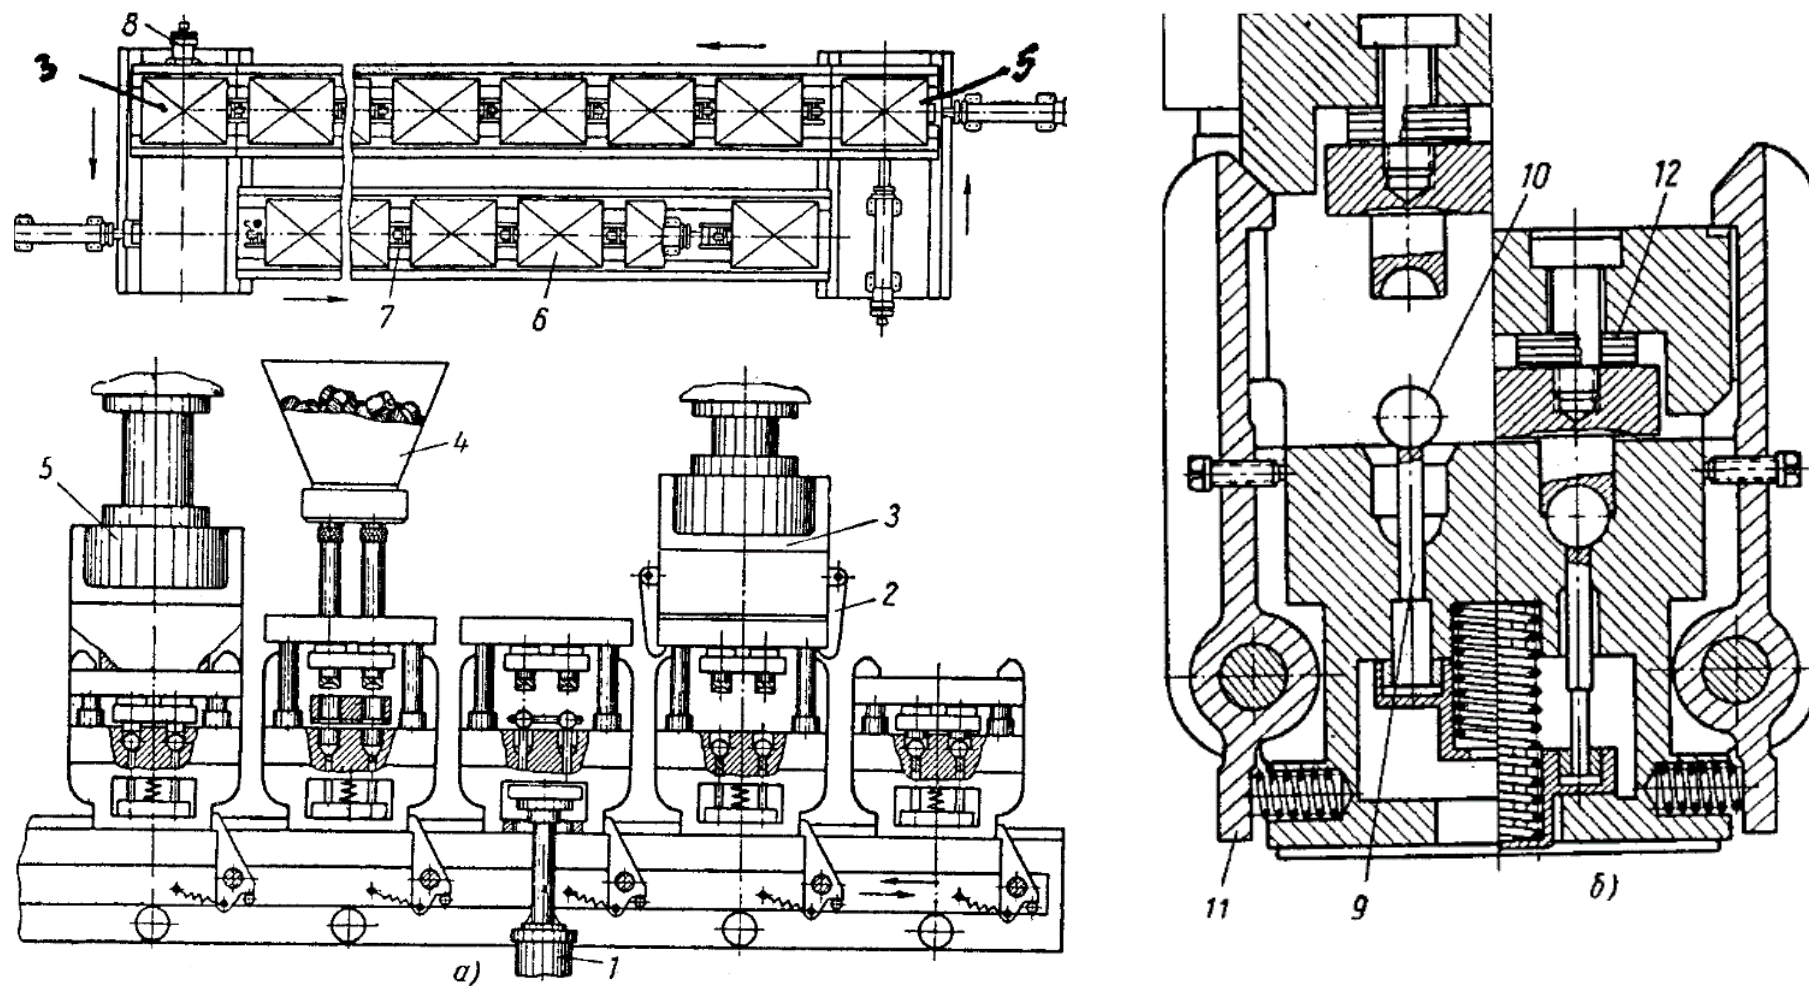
Автоматическая прессовая линия с выносными пресс-формами: *а* – общий вид; *б* – пресс-форма; 1 – гидроцилиндр выталкивания готовых изделий; 2 – захваты-держатели пуансона; 3 – пресс раскрытия пресс-формы; 4 – питатель загрузки таблеток; 5 – пресс смыкания пресс-формы; 6 – сомкнутые пресс-формы; 7 – транспортер; 8 – гидротолкатель; 9 – выталкиватель пресс-изделия; 10 – готовое пресс-изделие; 11 – рычаг замкового устройства; 12 – тарельчатая пружина
